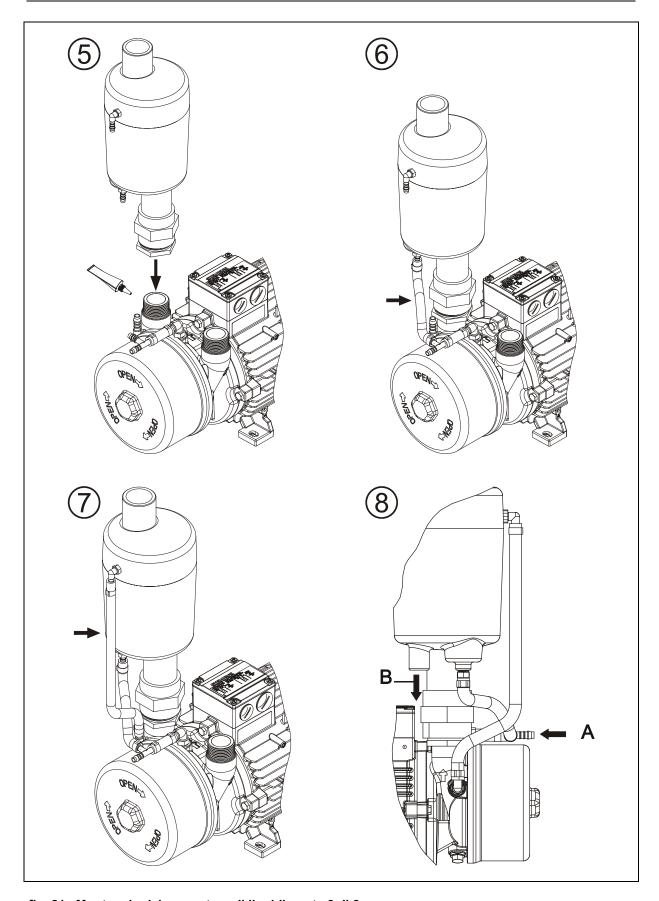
Montaggio del separatore di liquidi, parte 2 di 2
